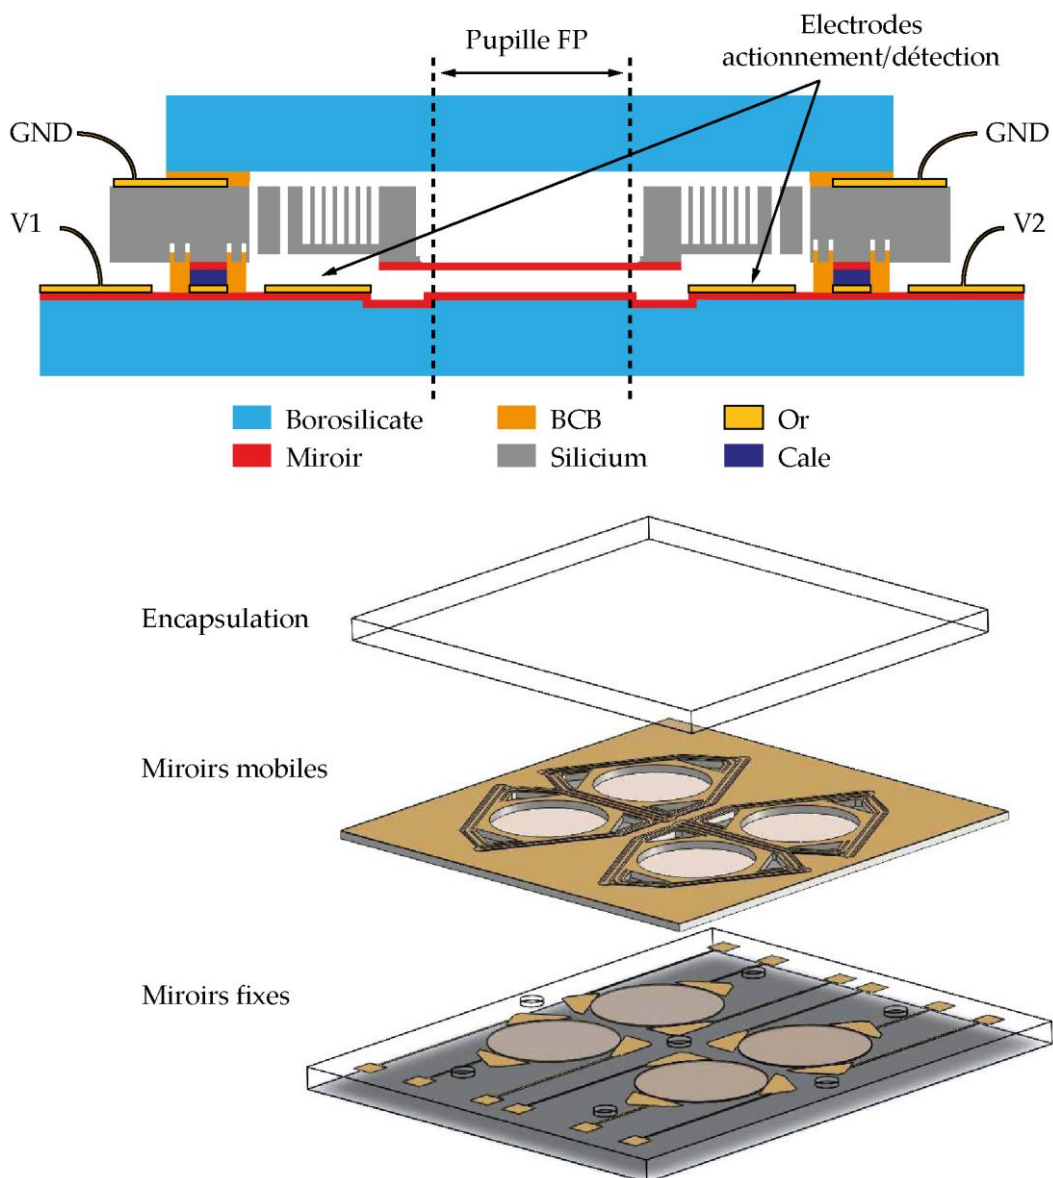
En haut, vue en coupe pour un filtre. En bas, vue 3D éclatée de l'assemblage envisagé.
